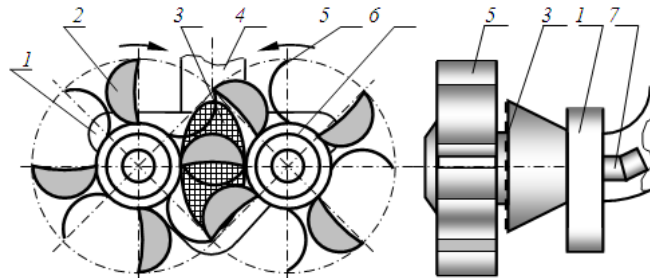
Схема двухроторного черпакового разрыхлителя.
